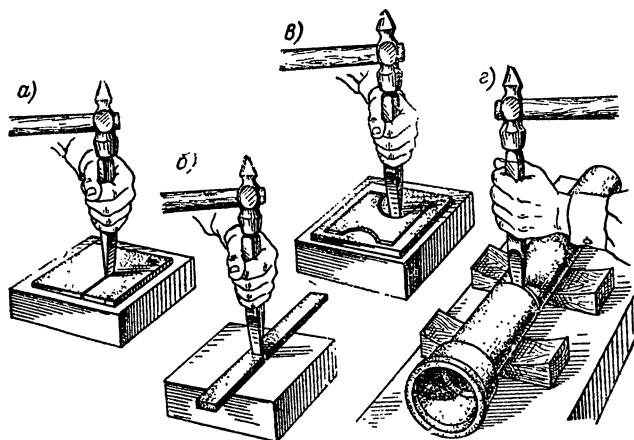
Рубка металла: а — листового материала; б — полосы; в — вырубание фигурной заготовки из листовой стали; г — перерубание чугунной трубы
